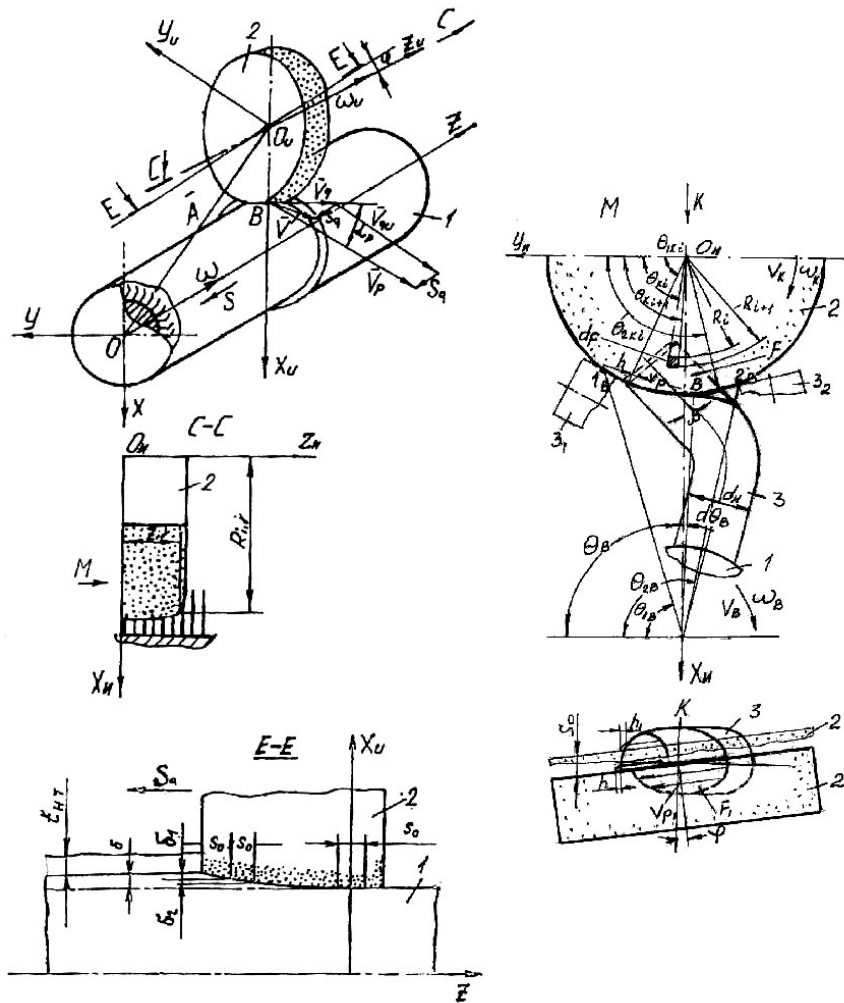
Схема шлифования игольчатой поверхности со скрещивающимися осями круга и рабочего валика
